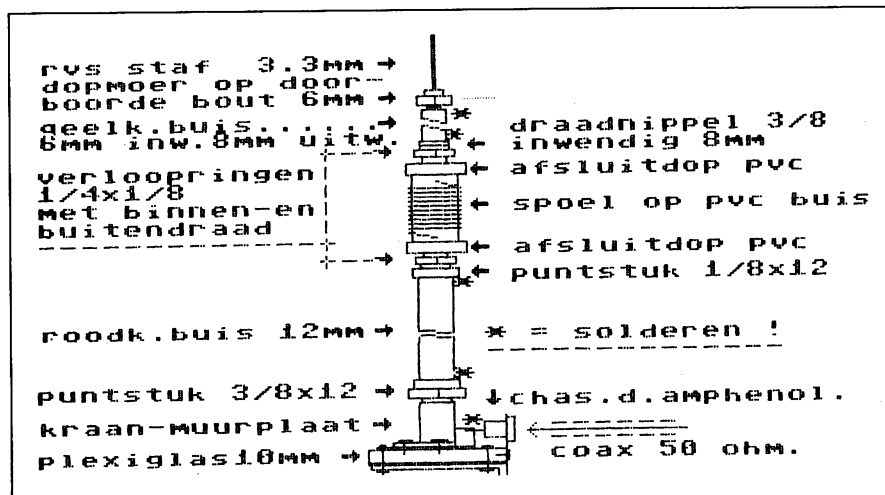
Naam, plaats en overzicht van de onderdelen.
